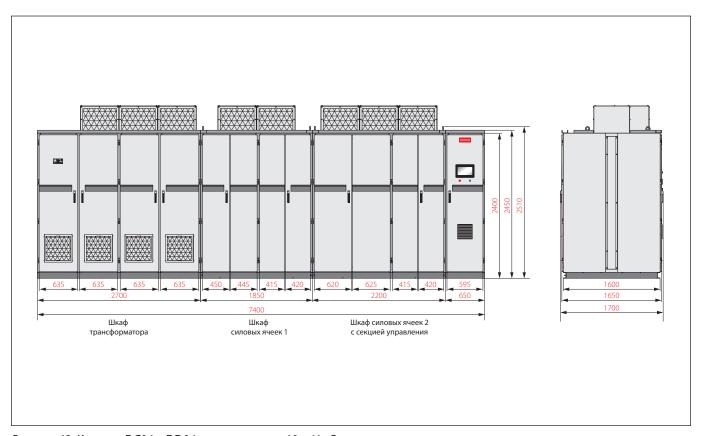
Корпуса DC04 и DD04 на напряжение 10 и 11 кВ
